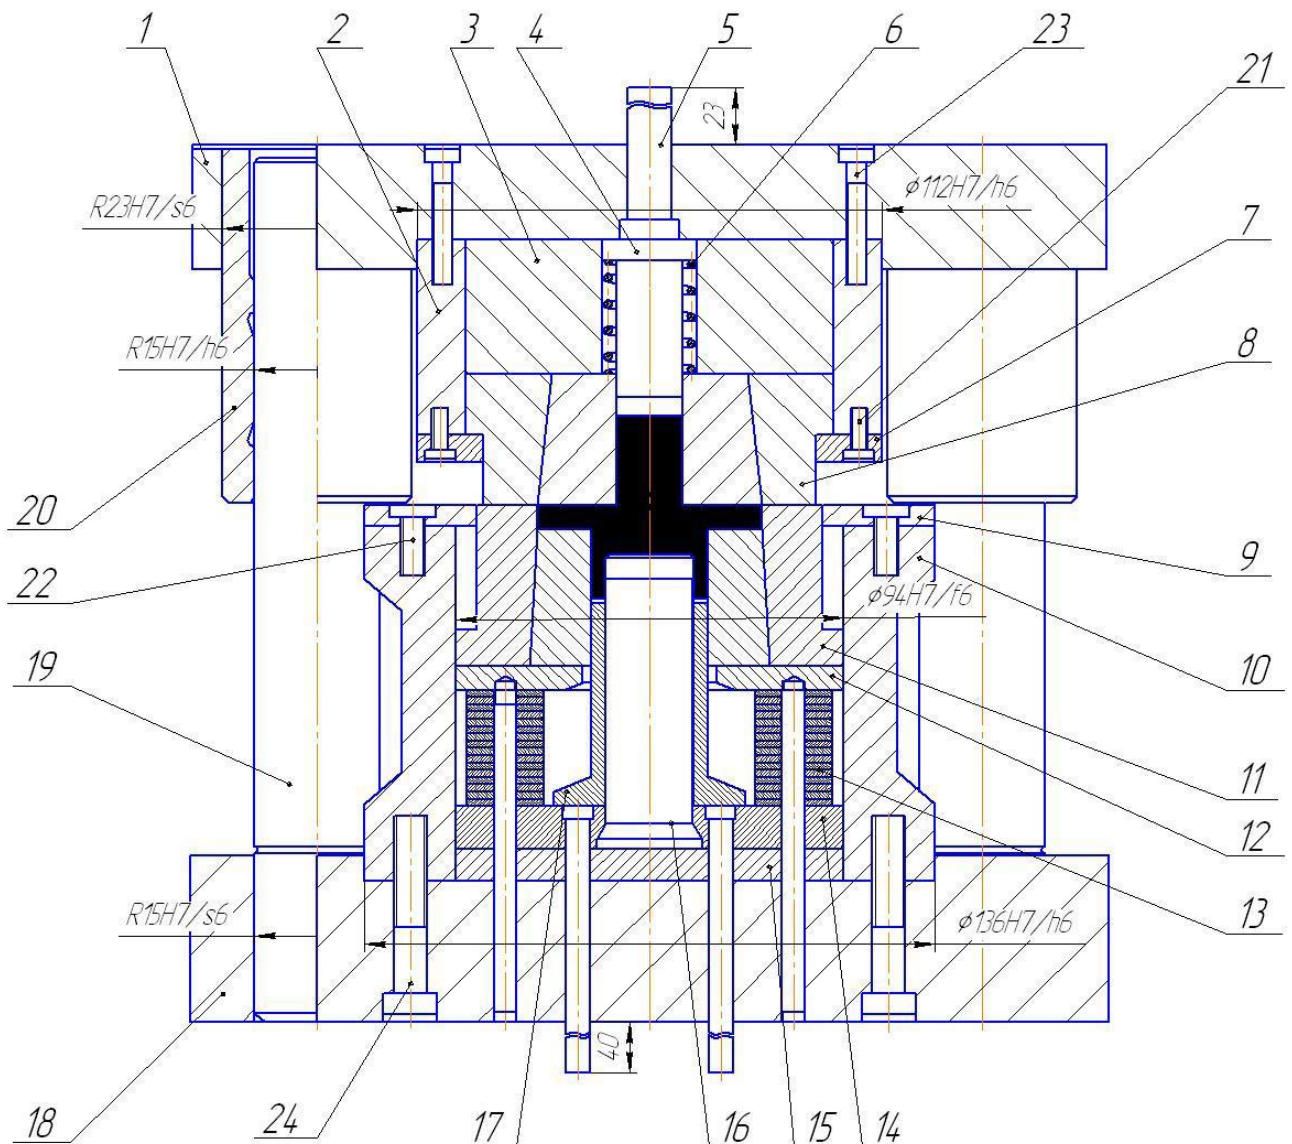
Схема штампу для комбінованого видавлювання
